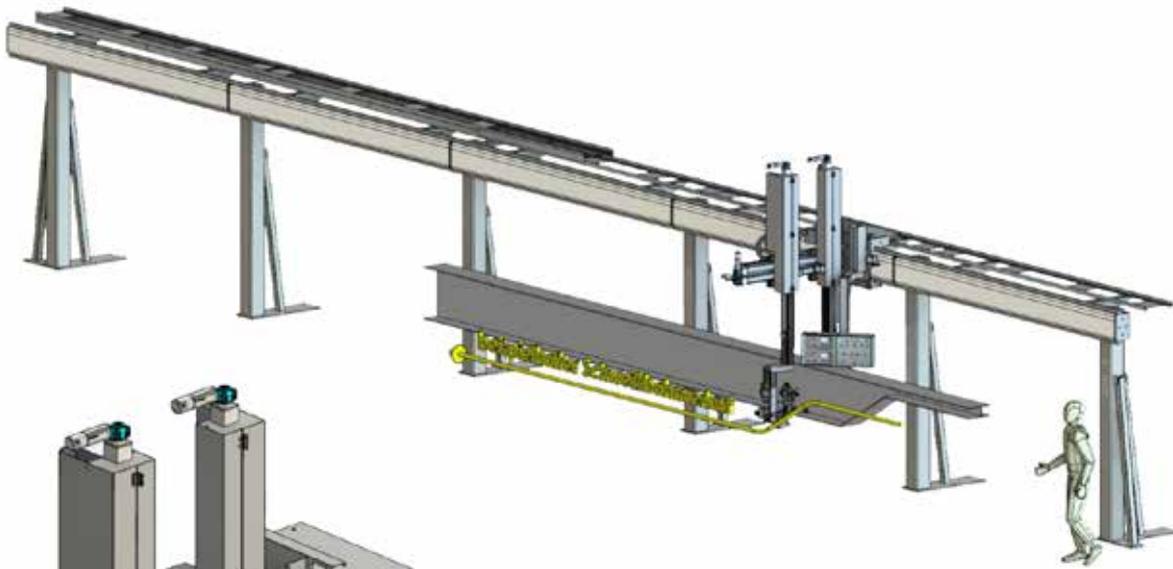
Trägerschweißvorrichtung 20 m
